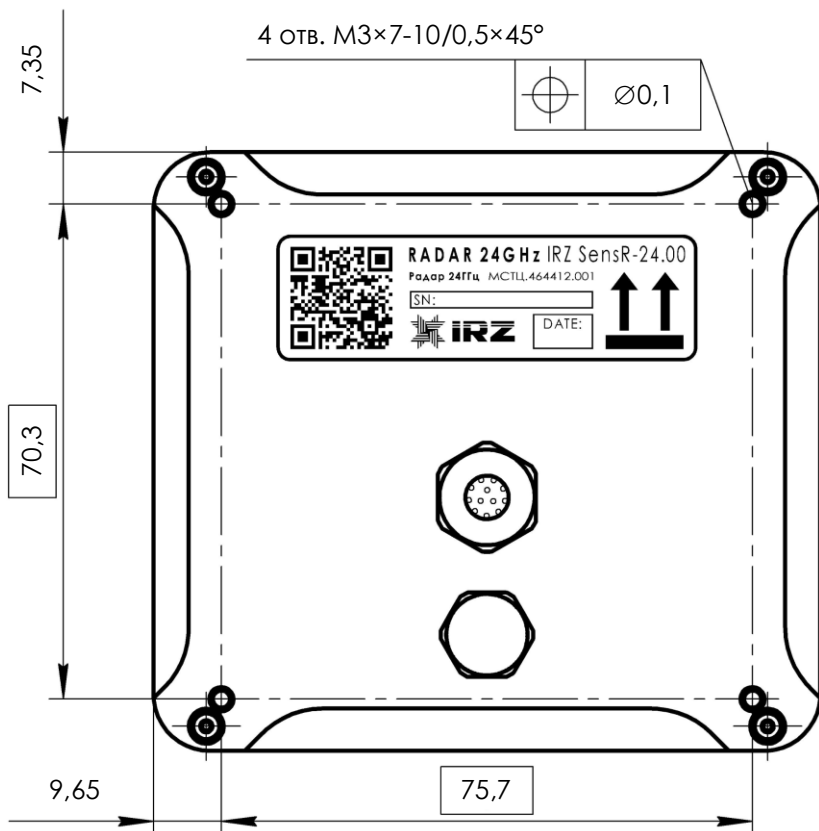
Расположение крепежных отверстий на корпусе изделия
